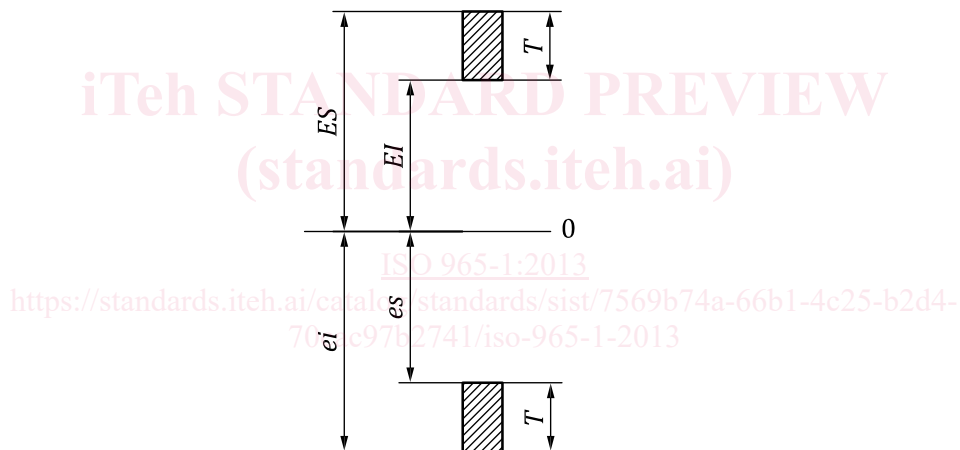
Расположение полей допусков относительно нулевой линии (номинальный размер)
